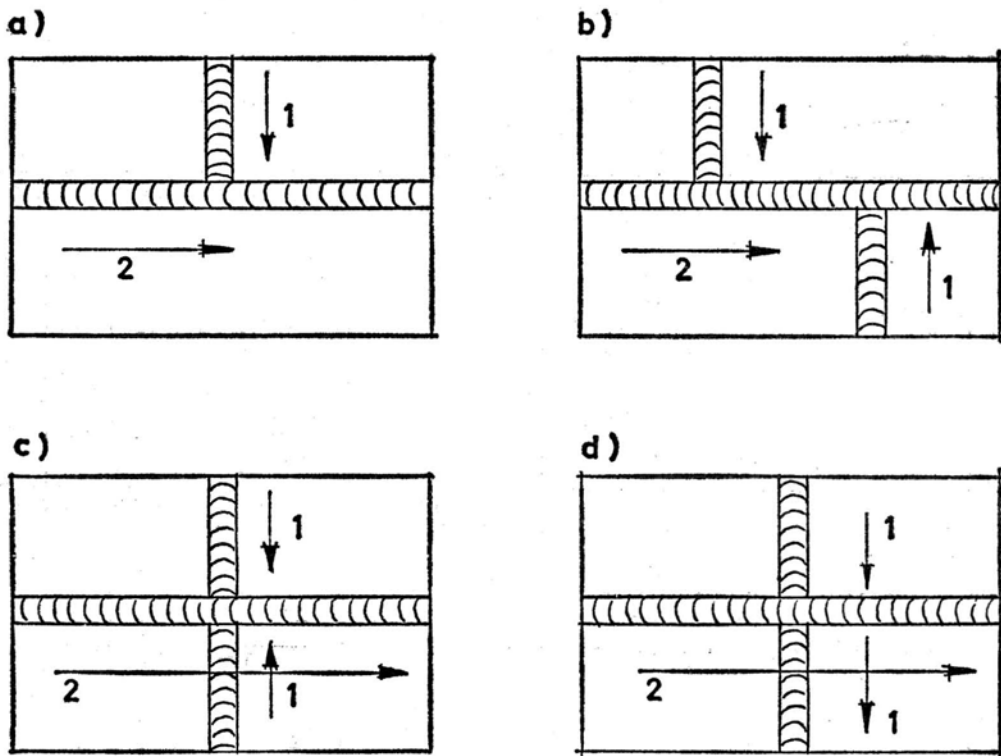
UNIONES PLANAS CON SOLDADURAS QUE SE CRUZAN
